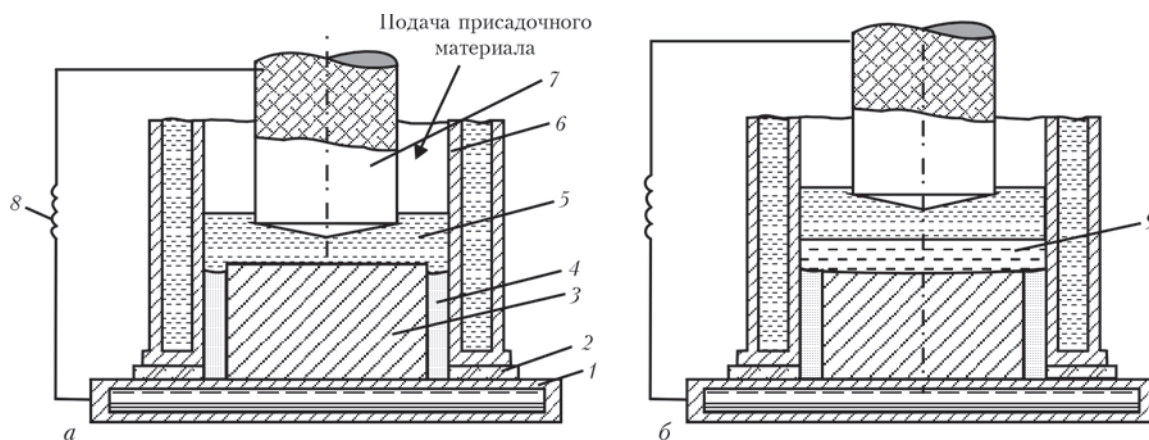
Схема горизонтальной ЭШН: а — перед началом подачи присадочного материала; б — после подачи присадочного материала. 1 — водоохлаждаемый поддон; 2 — диэлектрическая подкладка; 3 — наплавляемая заготовка; 4 — засыпка (сухой флюс); 5 — шлаковая ванна; 6 — кристаллизатор; 7 — графитированный электрод; 8 — источник питания; 9 — наплавленный металл
